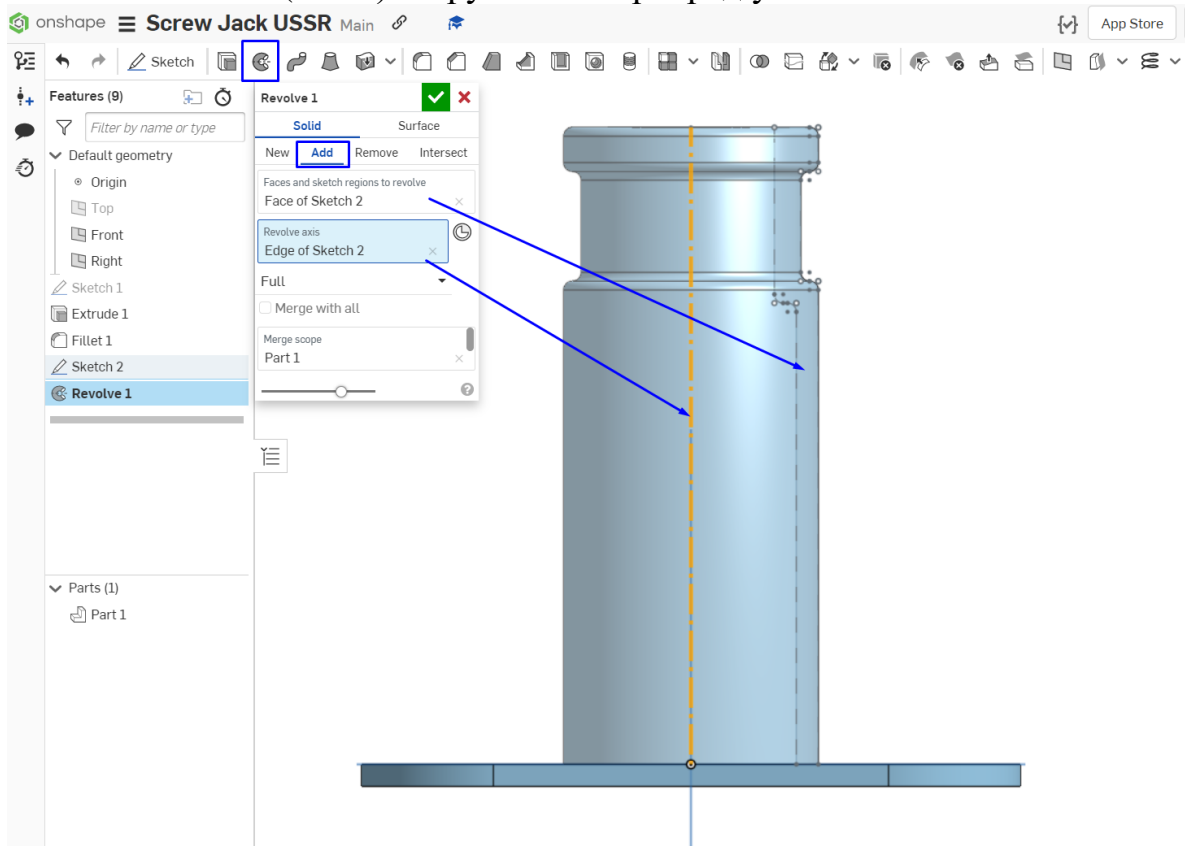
Використання операції (Revolve) для формування тіла обертання
